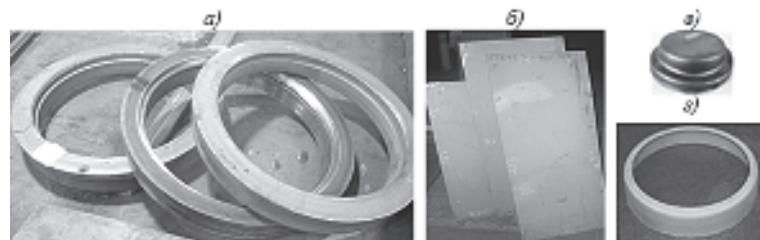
Полуфабрикаты и детали из сплава ВЖ172:
